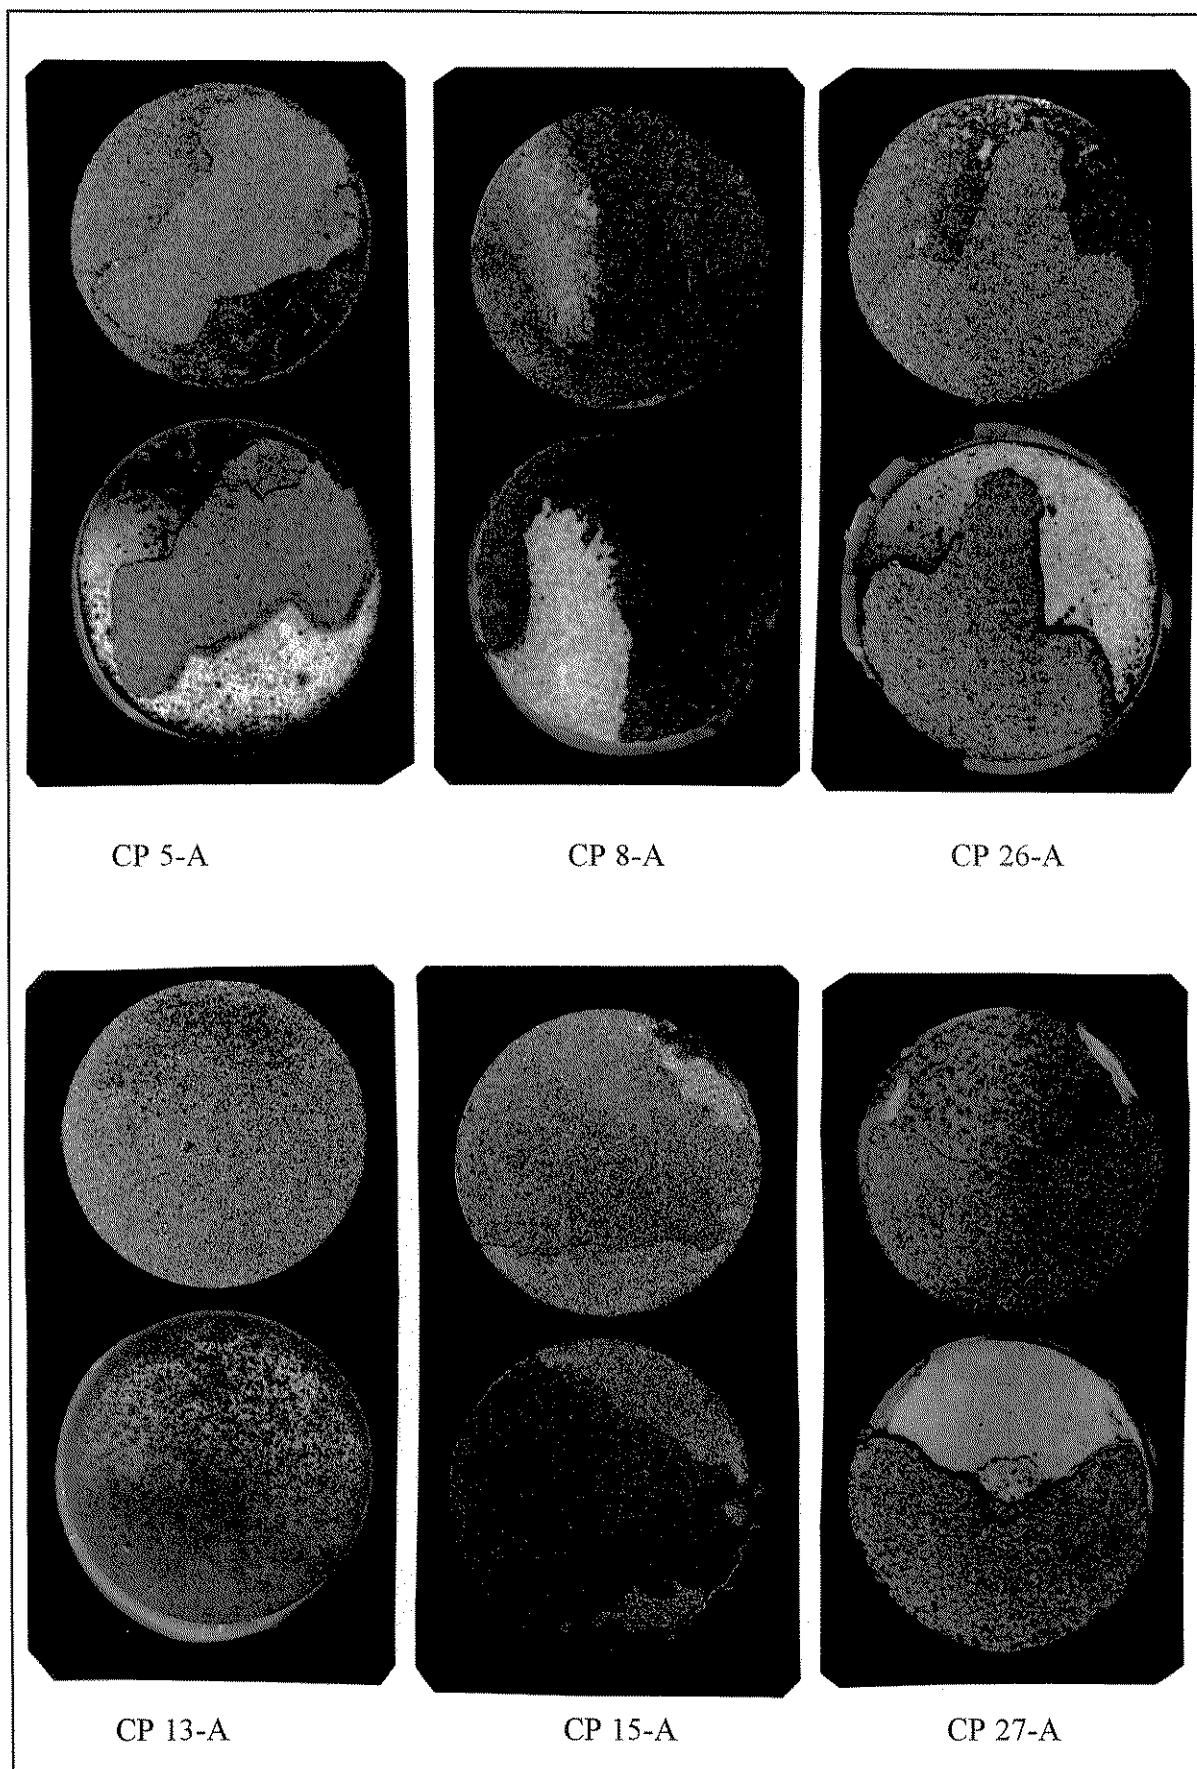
Superfícies de fratura - Ensaio ASTM- C-633 - Base 100-0
